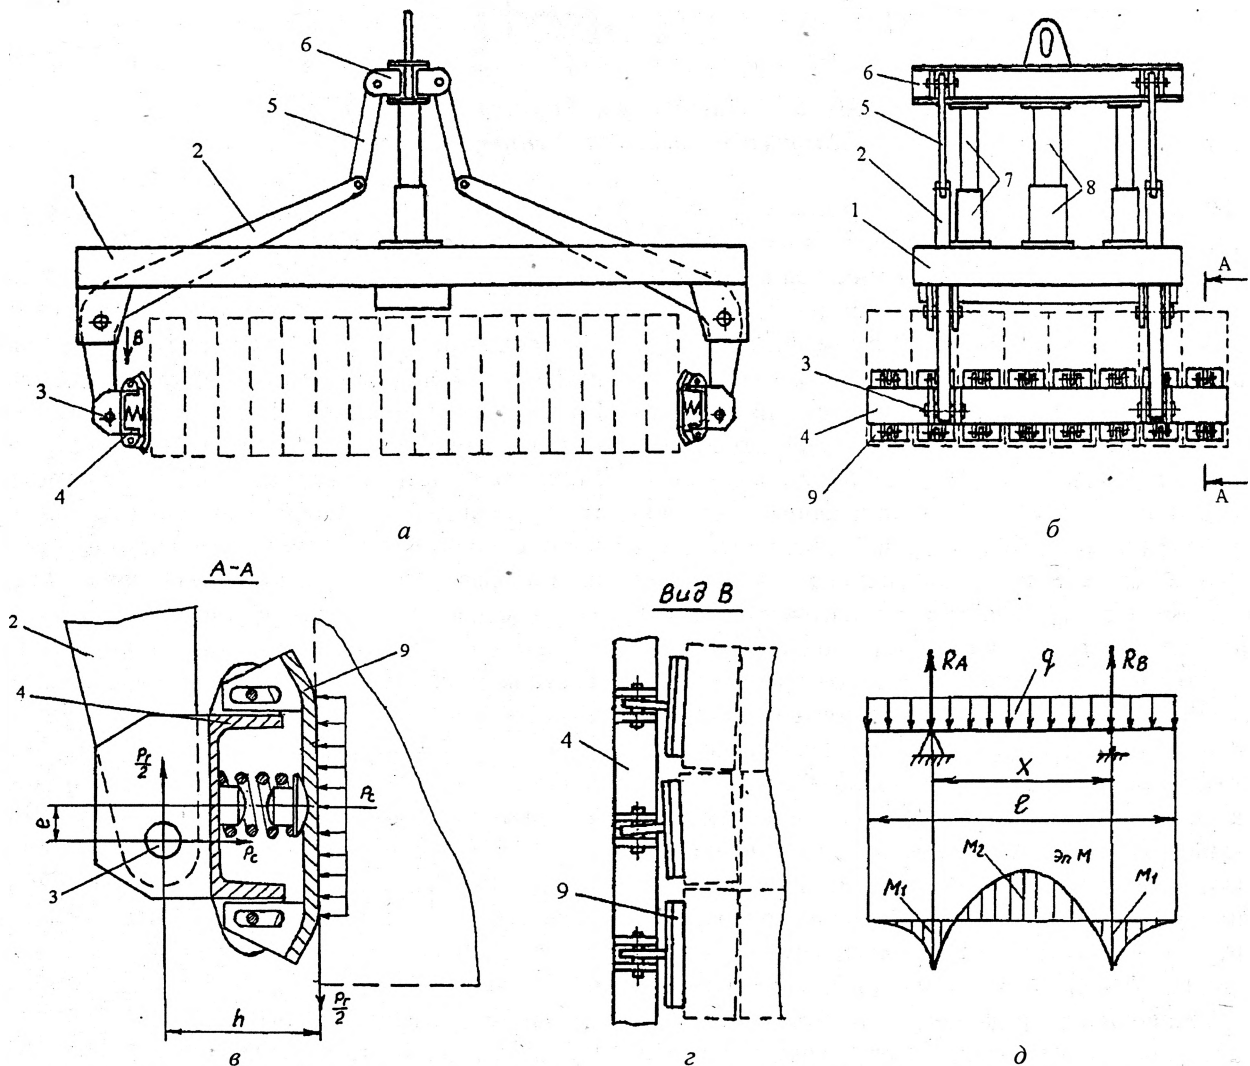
Автоматическое захватное устройство для блоков: а — вид сбоку; б — вид с торца; в — схема нагрузок, действующих на прижимную балку; г — схема расположения пружиненных башмаков при сжатии блоков; д — расчетная схема прижимной балки
